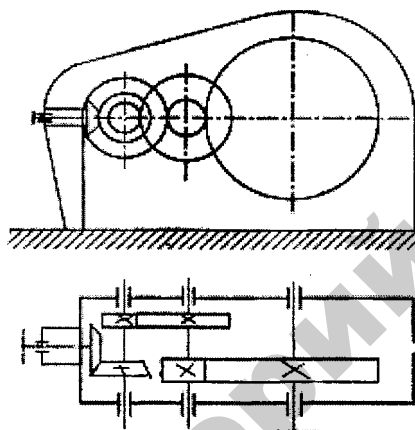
Схема трехступенчатого коническо-цилиндрического редуктора
